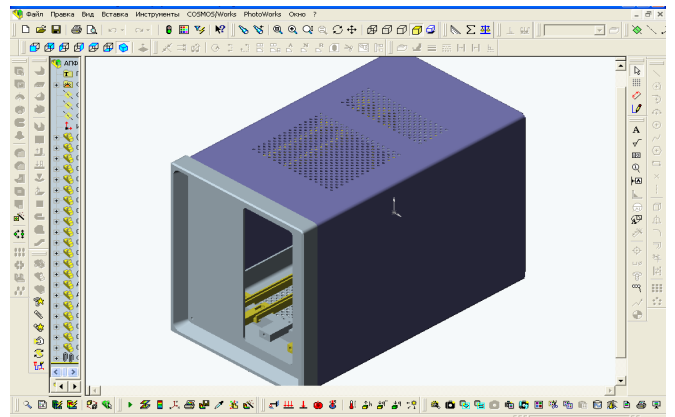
Корпус блока АПФС выполненный в САПР SolidWorks
